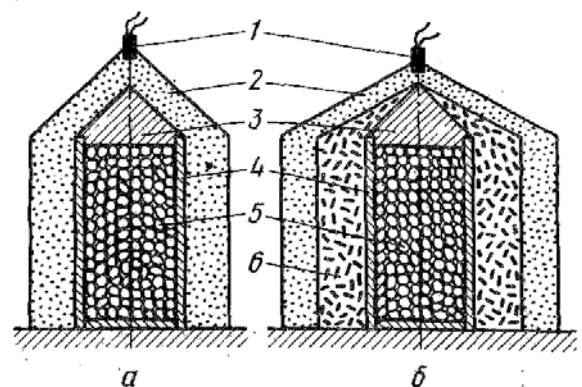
Схема взрывного прессования порошковых цилиндрических изделий
